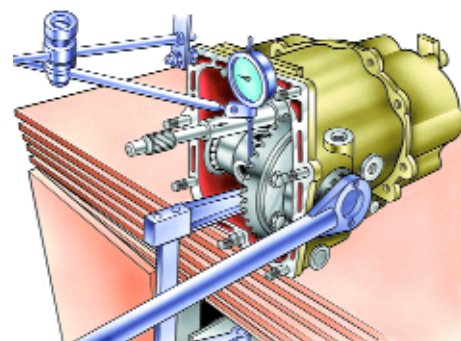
Проверка бокового зазора в зацеплении зубьев ведущей и ведомой шестерен главной передачи при помощи индикатора
